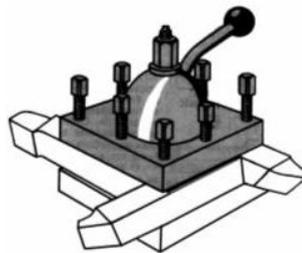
A torre pode ser equipada até 4 ferros de corte. Fonte - EEEP
